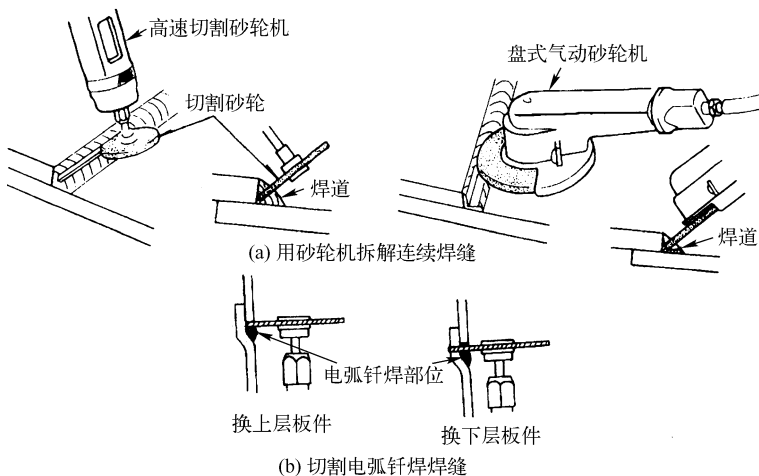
用砂轮机割断焊缝、拆解车身构件的方法
